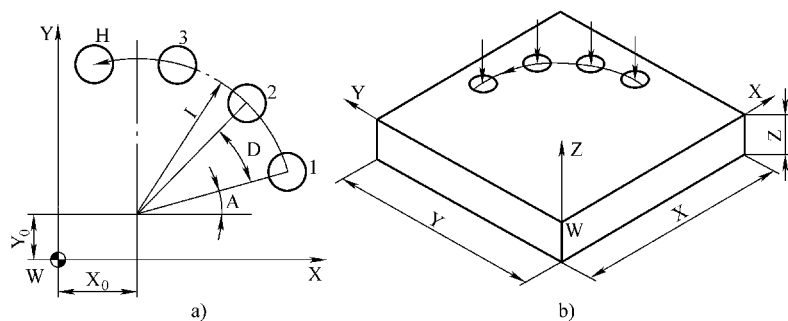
圆弧点阵孔群类零件钻削加工刀具路线示意图
